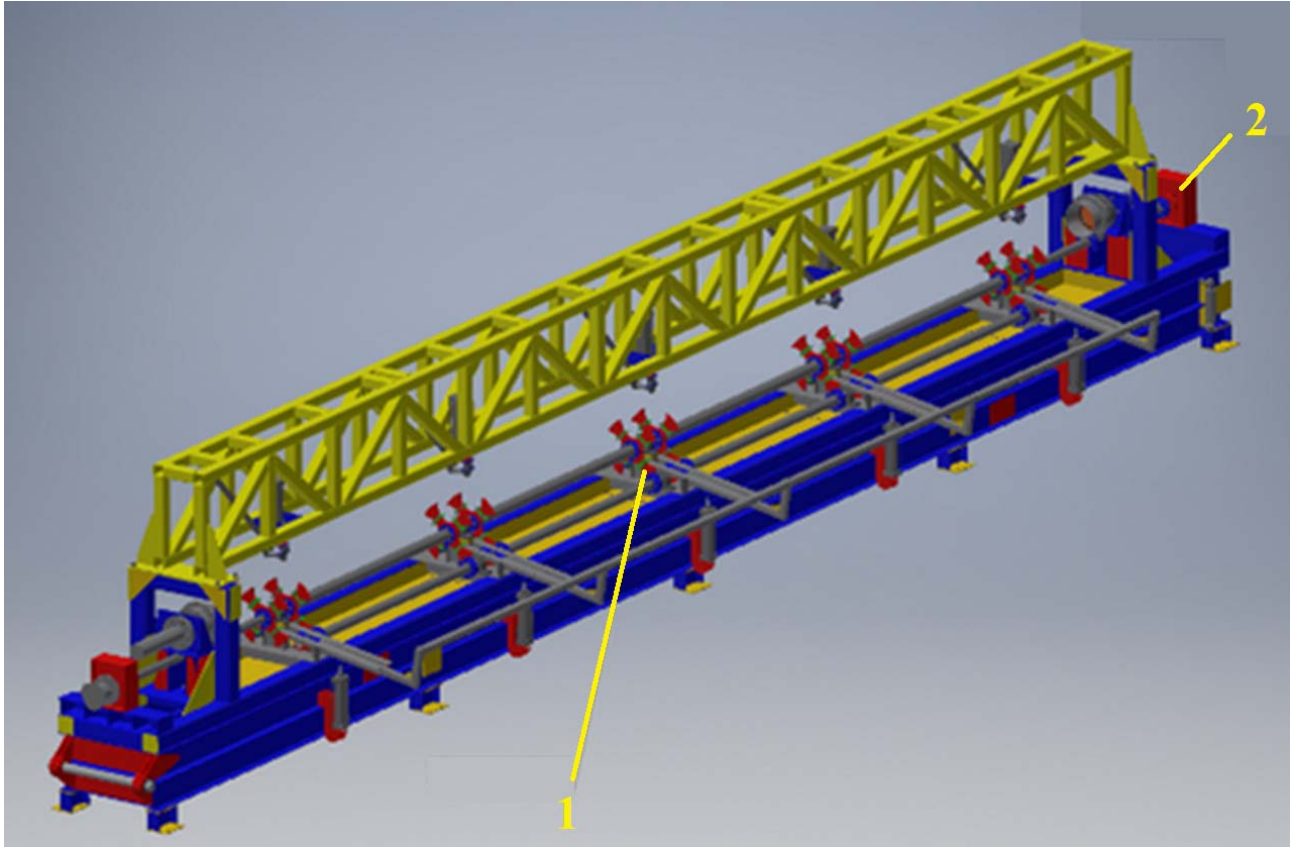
Загальний вид станда MetTerra СГИТ 01-89-219
